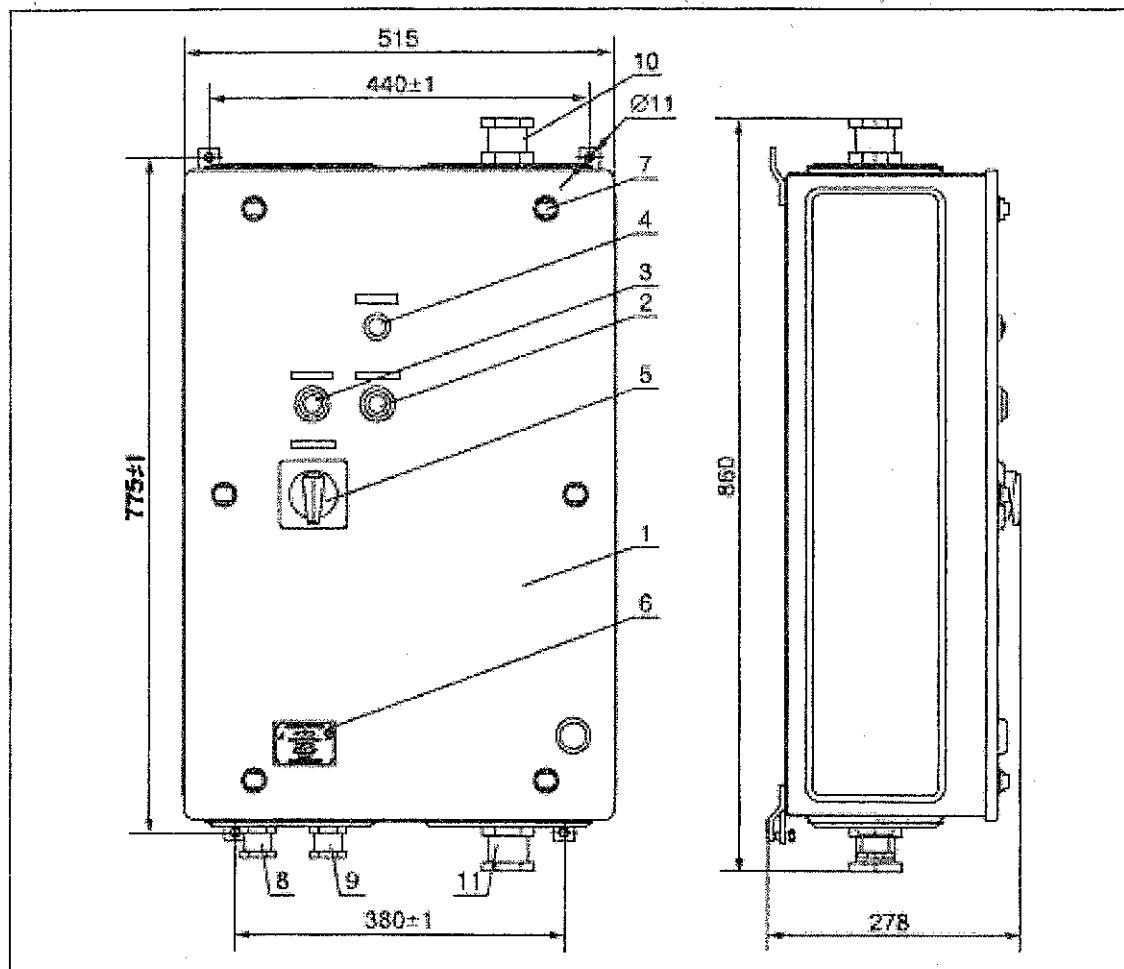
Общий вид и габаритные размеры ящика управления освещением ЯУО на токи 80-160 А
